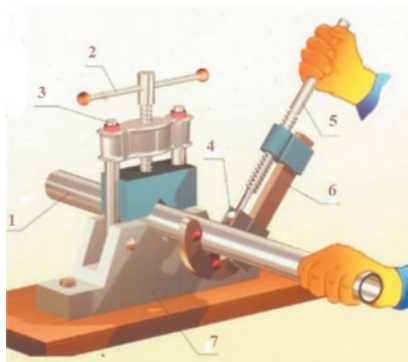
Труборіз: 1 — труба, 2 — рукоятка, 3 — гвинт, 4 — рухомий ролик, 5 — рукоятка труборіза, 6 — труборіз, 7 — притиск
